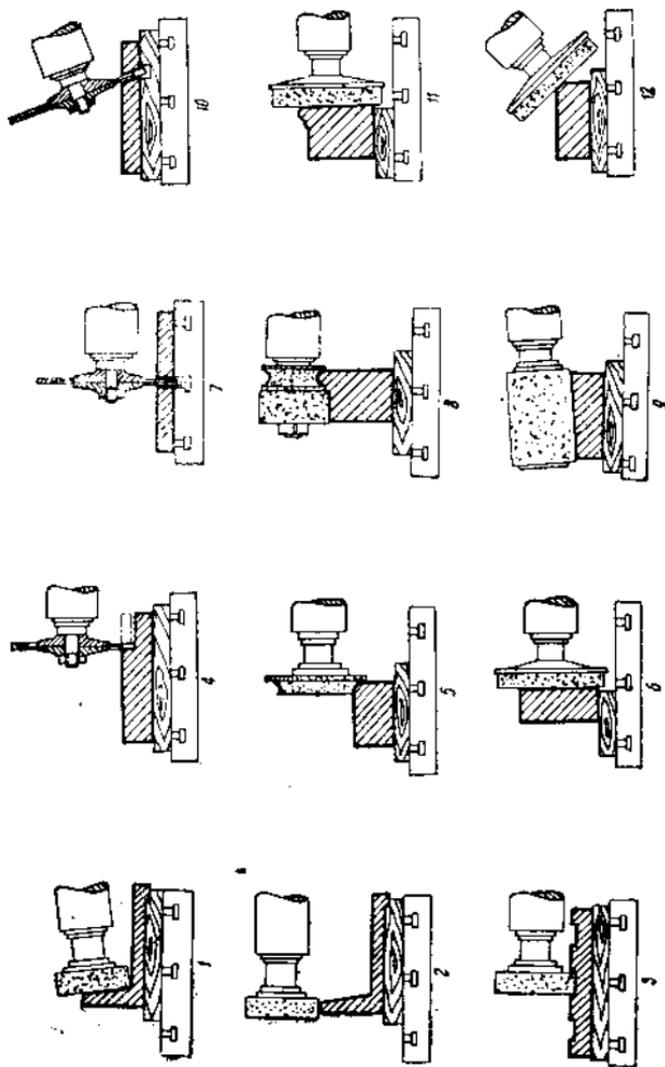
Различные виды обработки на универсальном фрезерном станке
